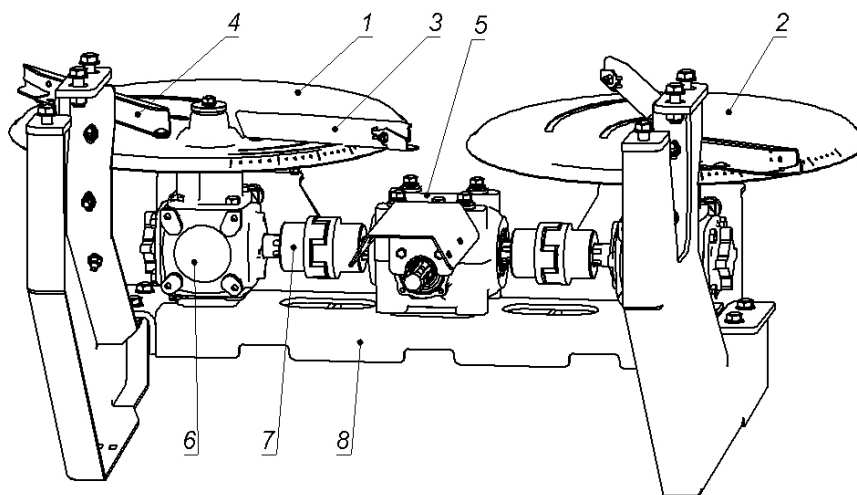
Разбрасывающий механизм (тарелки с редукторной балкой)
